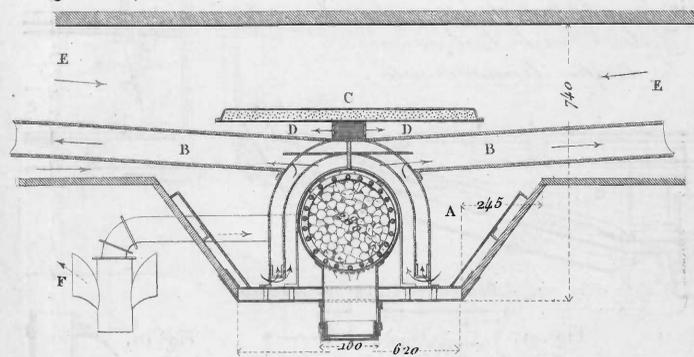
Appareil à air chaud du Nord-Est suisse. Coupe transversale.
